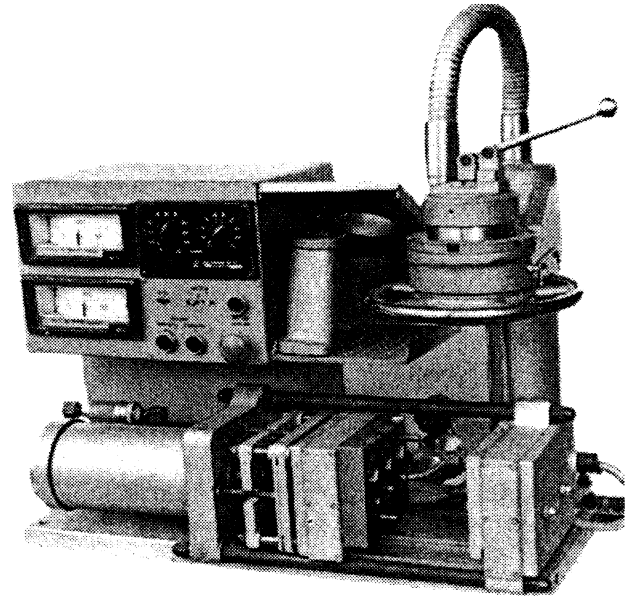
Лабораторная установка мод. 4735БМ для изготовления стандартных измерительных образцов типа «восьмерка» и «балочка»
